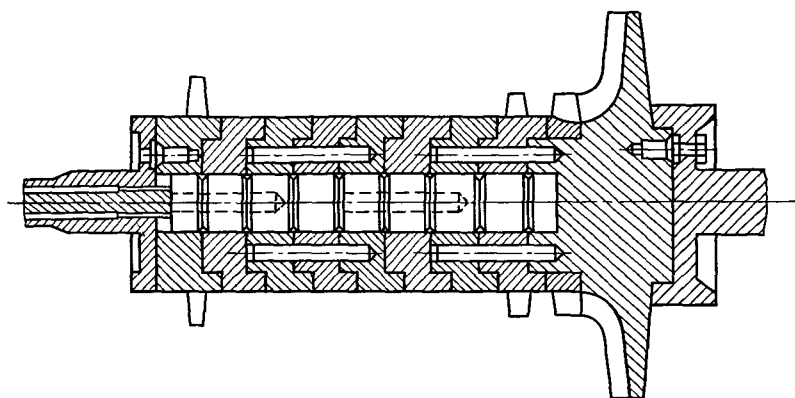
Дисковый наборный ротор с призонными пальцами осевого компрессора ГТУ фирмы Центтракс
